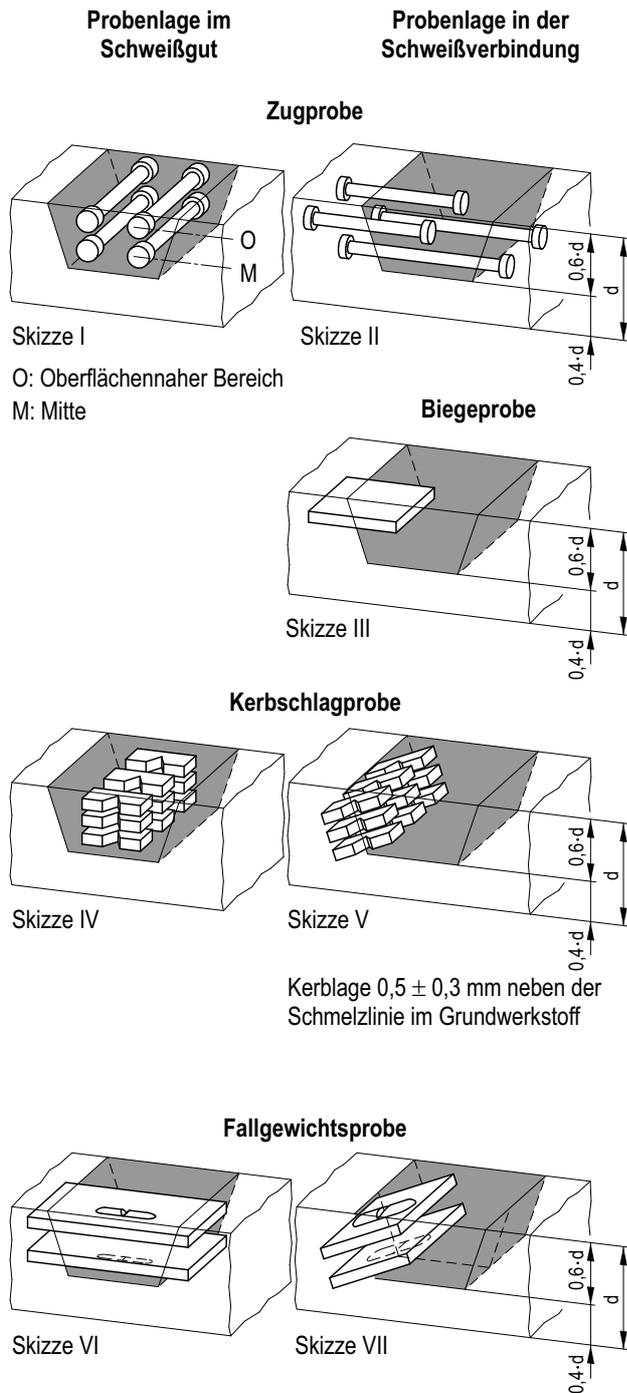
Probenentnahme bei Verfahrensprüfungen für Ausmuldungsschweißungen
